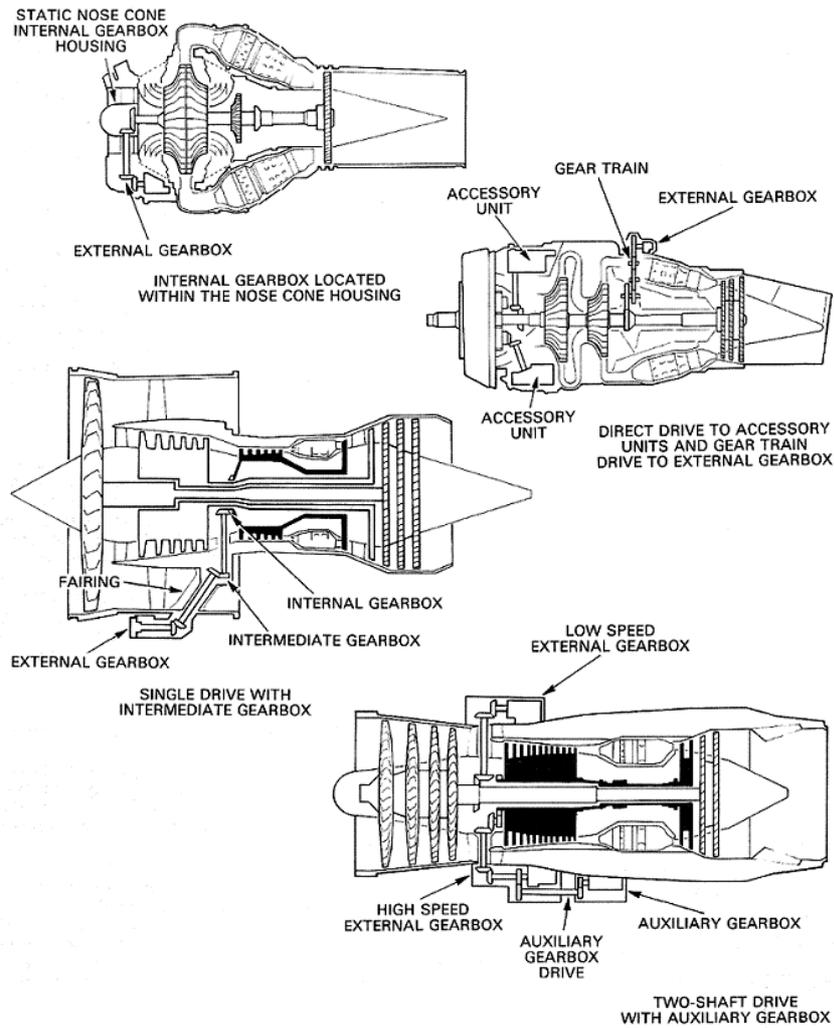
". - Acoplamiento mecánico entre motor y cajas de accesorios.
